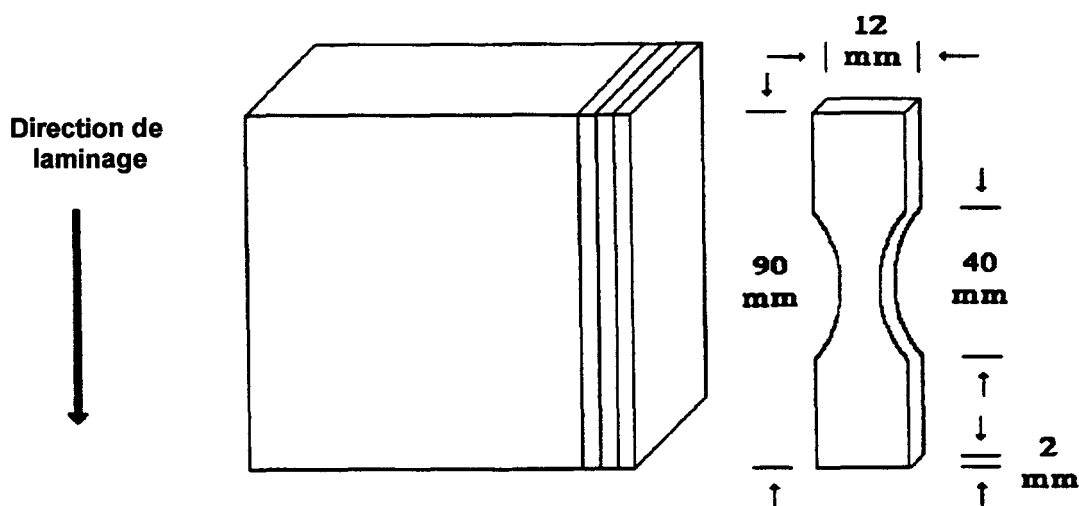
Forme et dimensions des échantillons testés en fatigue.
